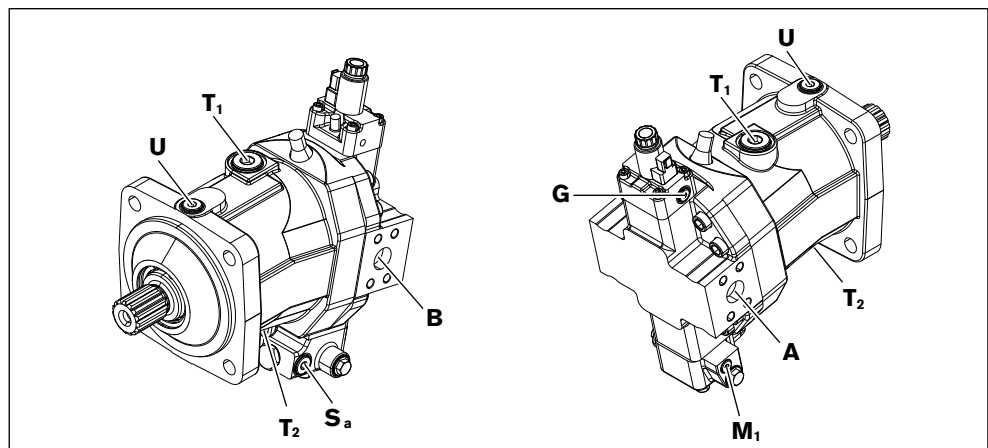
Vue d'ensemble des raccords A6VM avec réglage EP5/EP6 et valve de rinçage, raccords de service sur le côté
